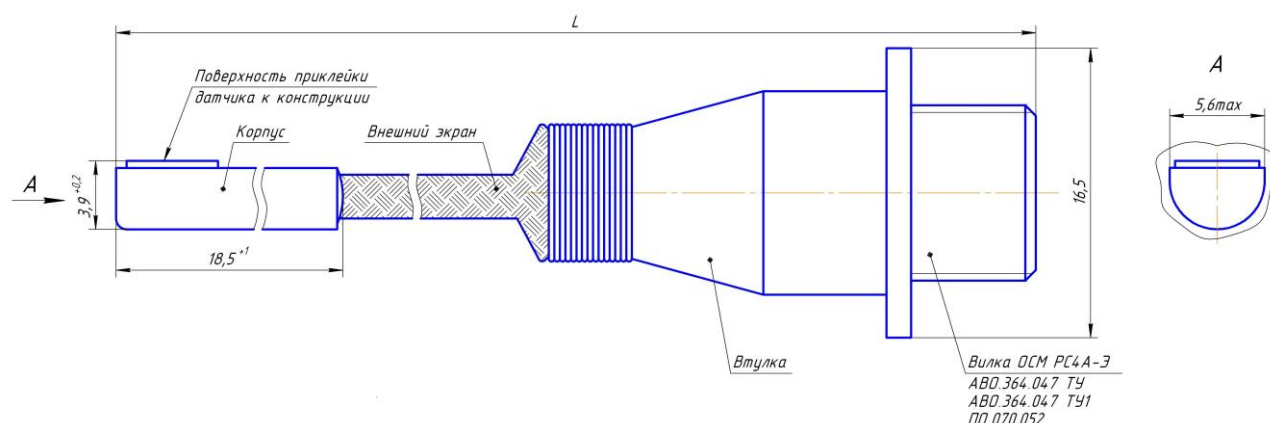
Габаритные и установочные размеры датчика исполнений ЦДТ 1 – ЦДТ 1-05
